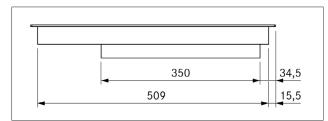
Dimensões do aparelho PKCH3, vista lateral
